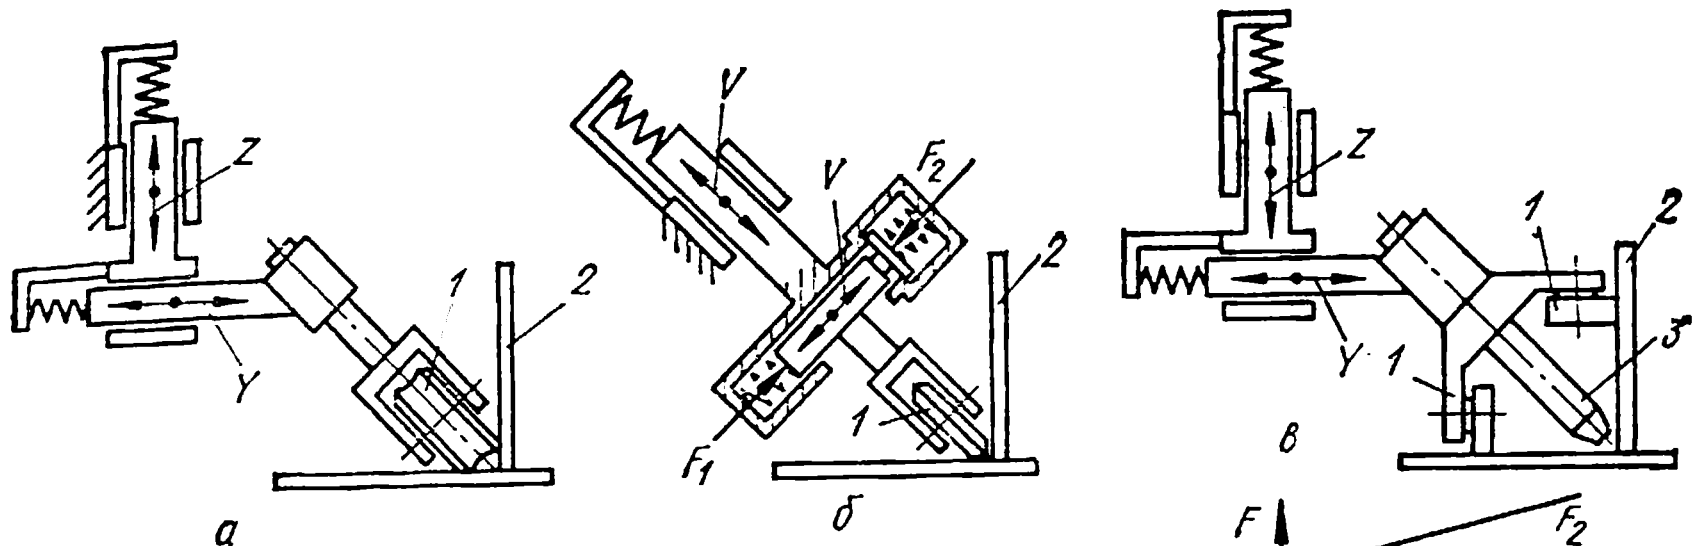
Схемы двухкоординатных устройств прямого действия для сварки угловых швов:
